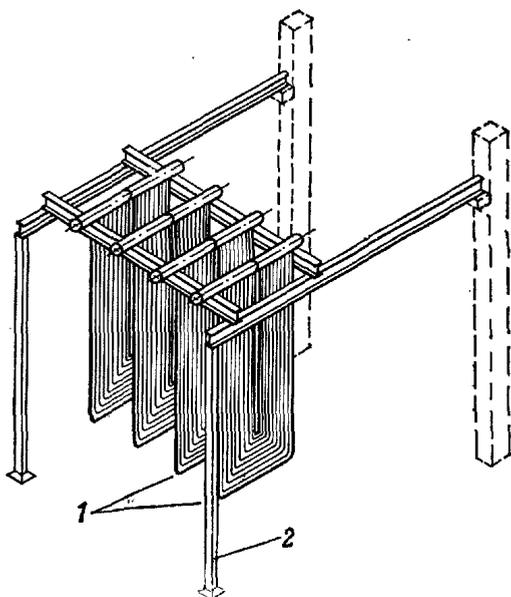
Укрупнительная сборка блоков ширм в вертикальном положении
